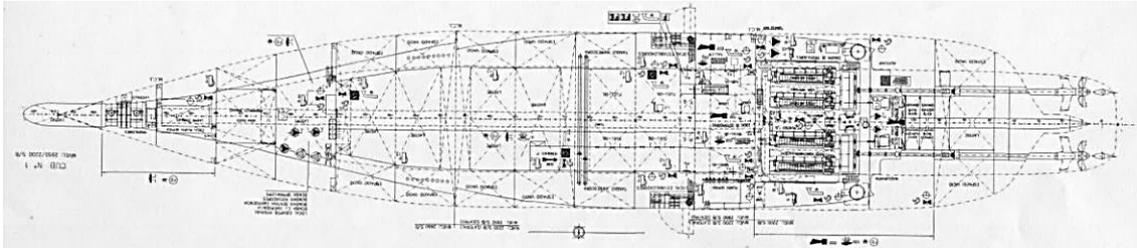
Plano de cubierta con elementos de máquinas del Ciudad Autónoma Melilla.
